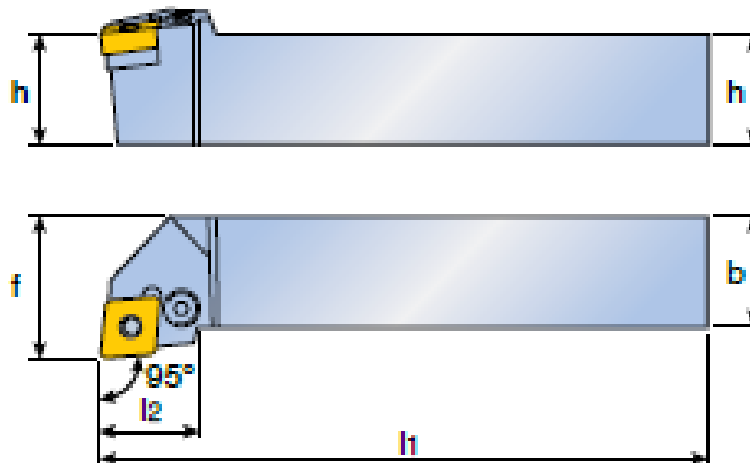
Образец режущего инструмента компании SANDVIK
